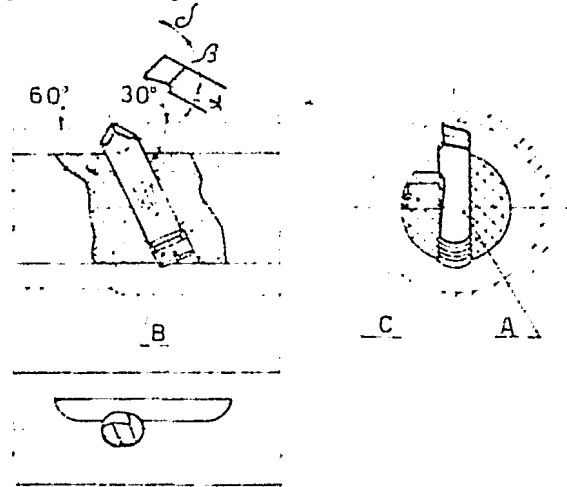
Mandril con herramienta regulable para mandrinado de desbaste.
